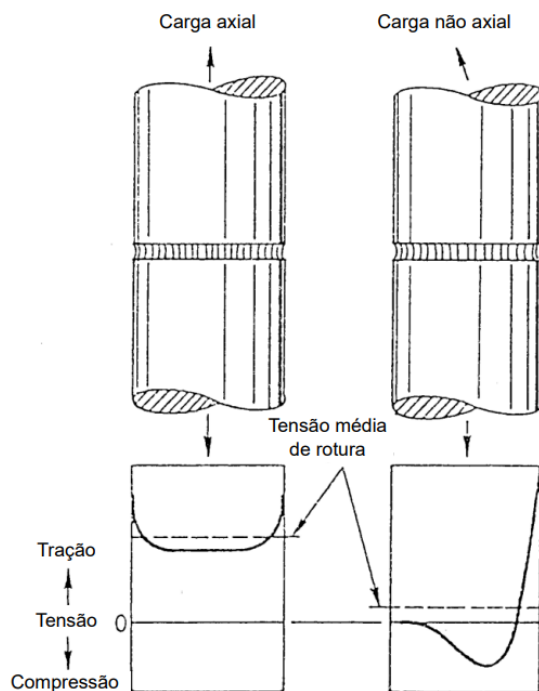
Distribuição de tensões numa junta adesiva tubular solicitada sob a forma axial (esquerda) e não axial (direita). Adaptado de Petrie [2].
